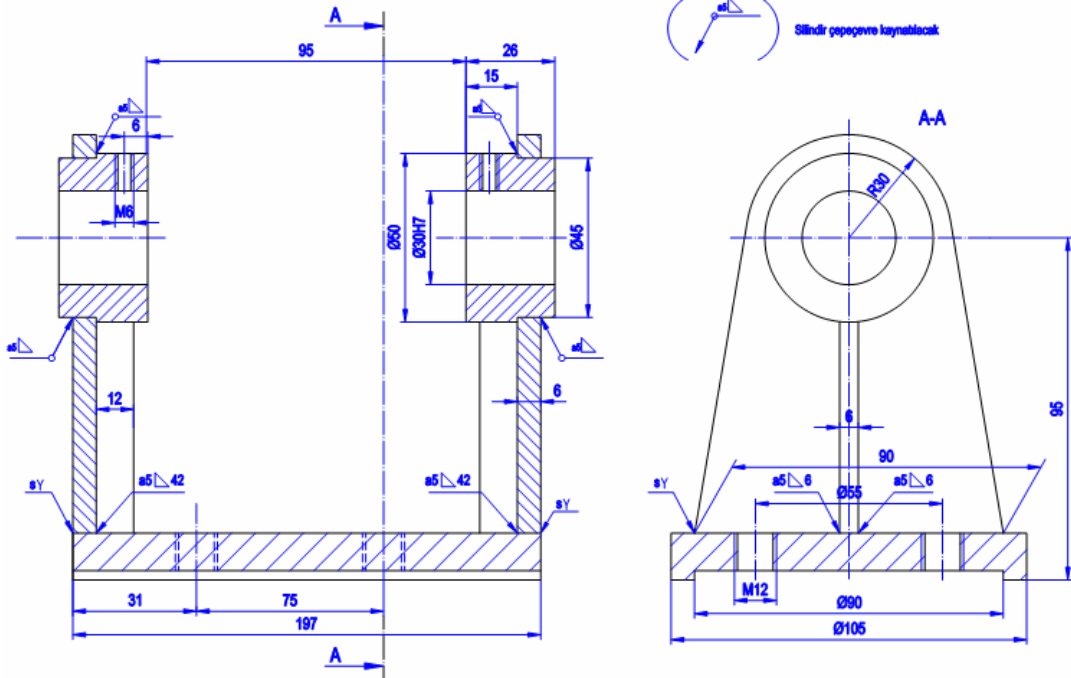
Kaynak dikişlerinin işaretle gösterilmesi
